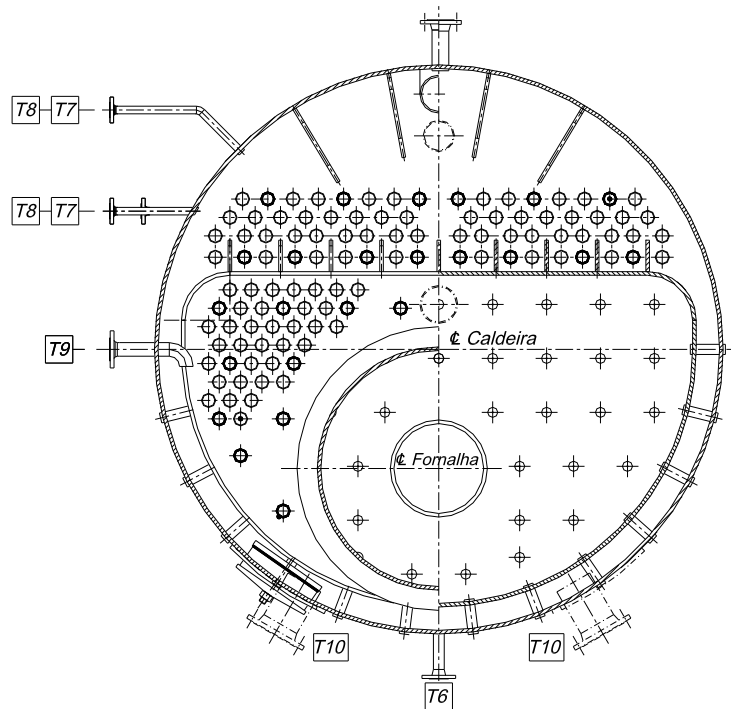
Equipamento e tubuladuras de uma caldeira.
